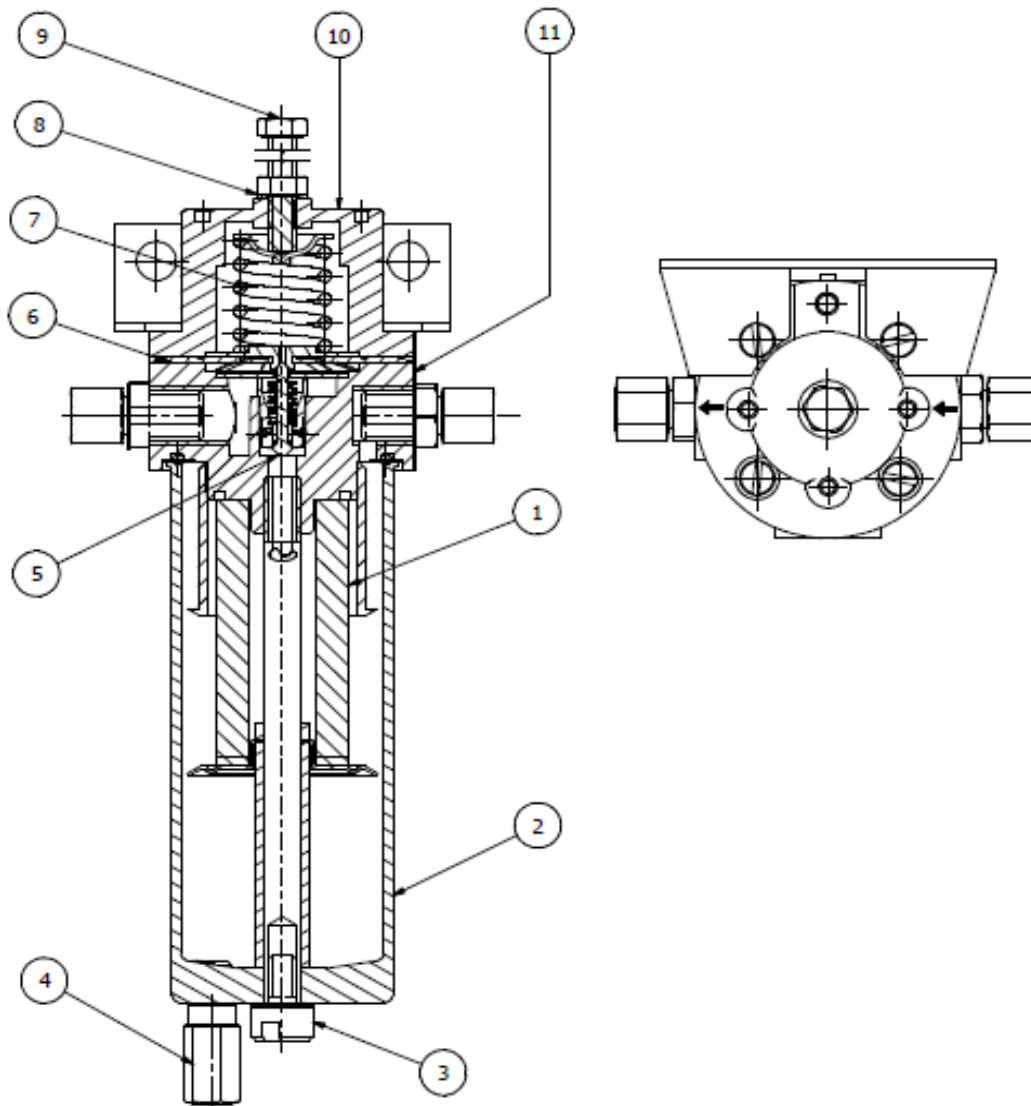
Функциональная схема редуктора. 1 - керамический фильтр; 2 - резервуар; 3 - болт соединительный; 4 - предохранительный клапан; 5 - регулирующий клапан; 6 - мембрана; 7 - установочная пружина; 8 - стопорная гайка; 9 - регулировочный винт; 10 - корпус пружины; 11 - корпус клапана
